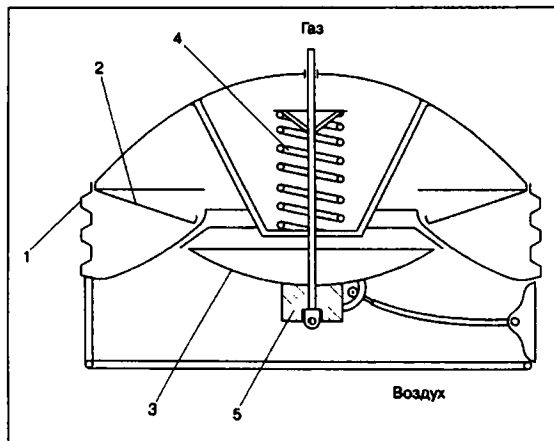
Автоматический газовый клапан дирижабля LZ-129: 1 — алюминиевый обод; 2 — резиновая мембрана; 3 — тарелка; 4 — пружина; 5 — груз
